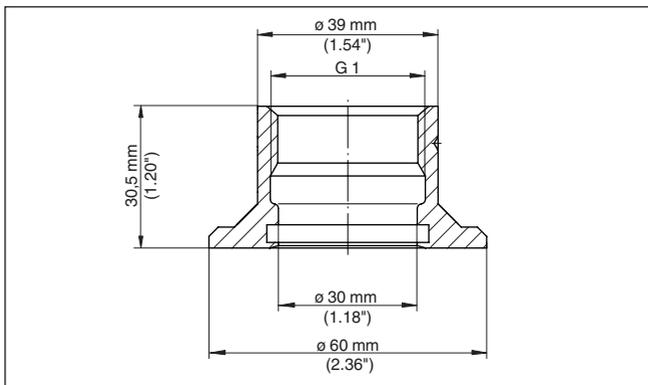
Medidas da luva para soldagem G1 (DIN 3852-X) - adequada para produtos alimentícios
